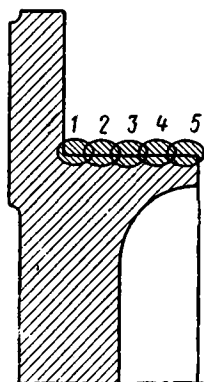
Последовательность наложения сварных валиков при наплавке посадочной поверхности подшпникового щита.
